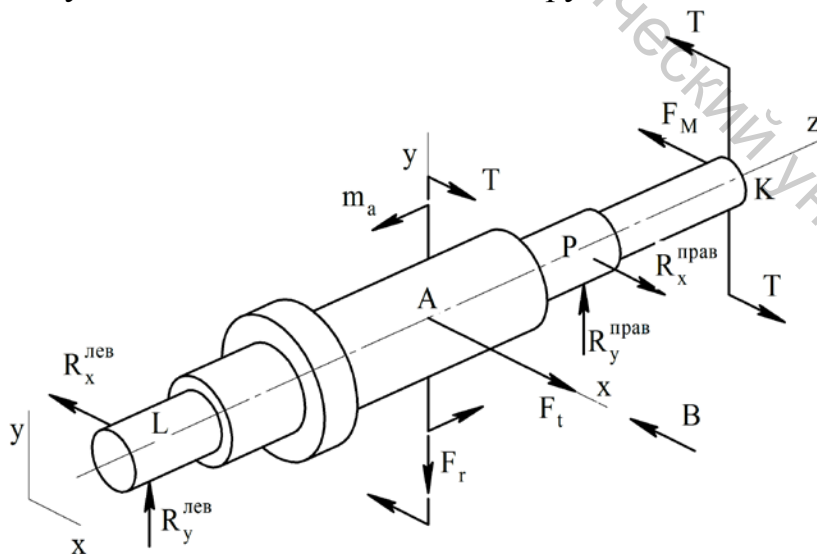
Силы, действующие на тихоходный вал одноступенчатого цилиндрического косозубого редуктора
